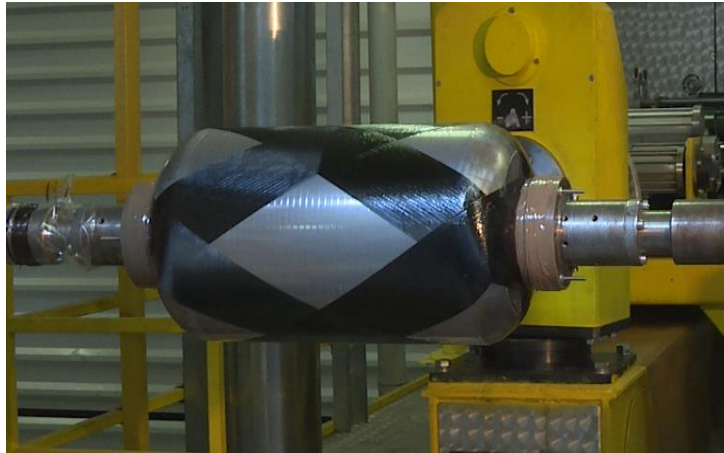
Процес намотування силової оболонки корпусу паливного бака
